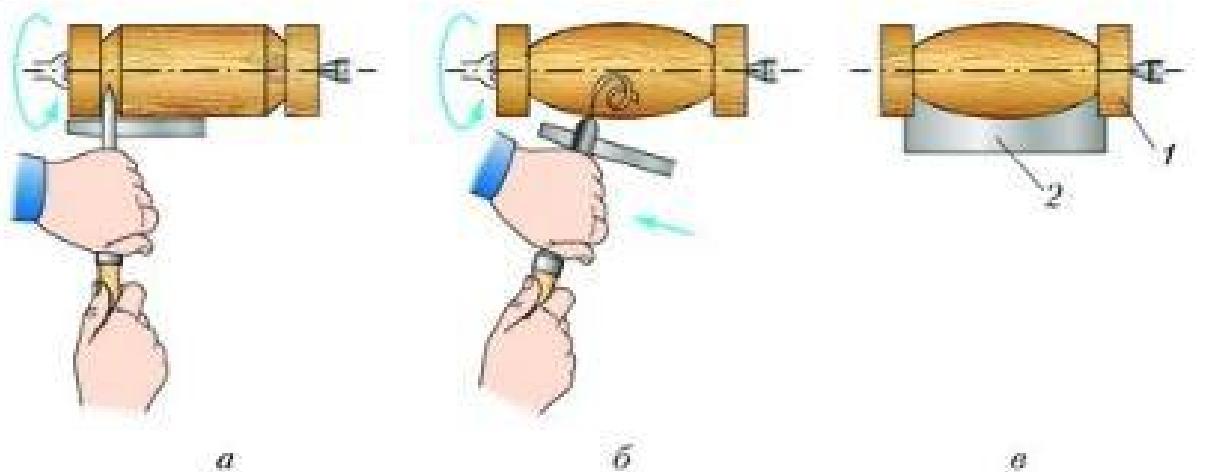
Обработка выпуклой поверхности: *а* – подрезание внутренних торцов; *б* – черновое точение; *в* – проверка формы поверхности шаблоном;
